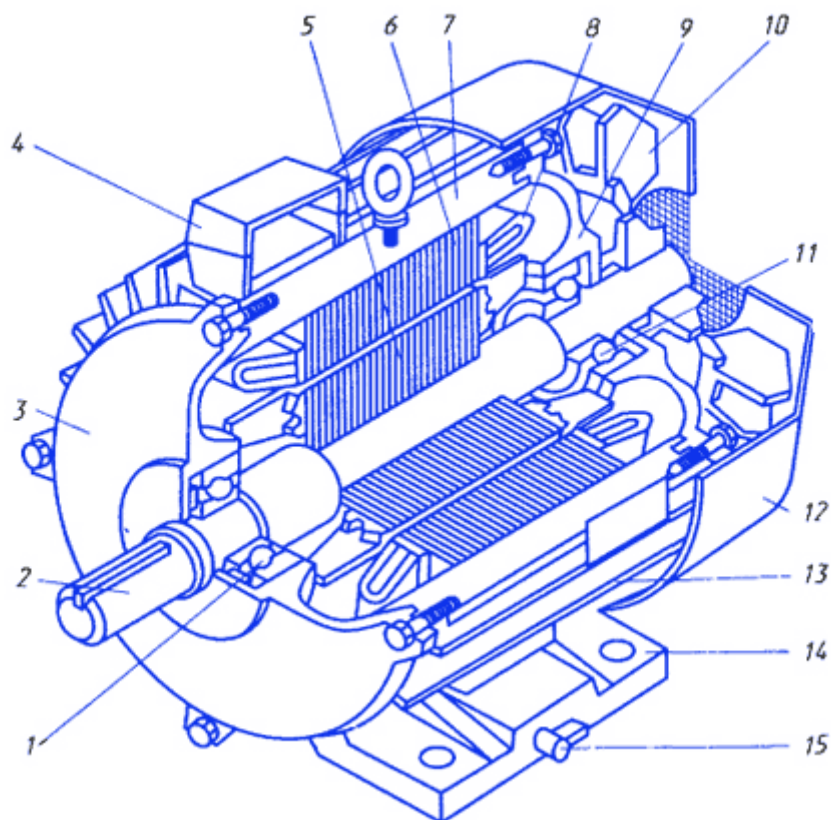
Общий вид и конструкция трехфазного асинхронного двигателя:
